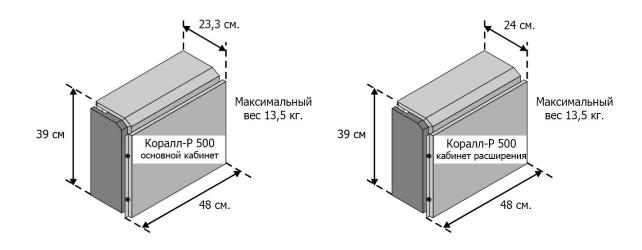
Габаритные размеры корзин Коралл-Р 500.
